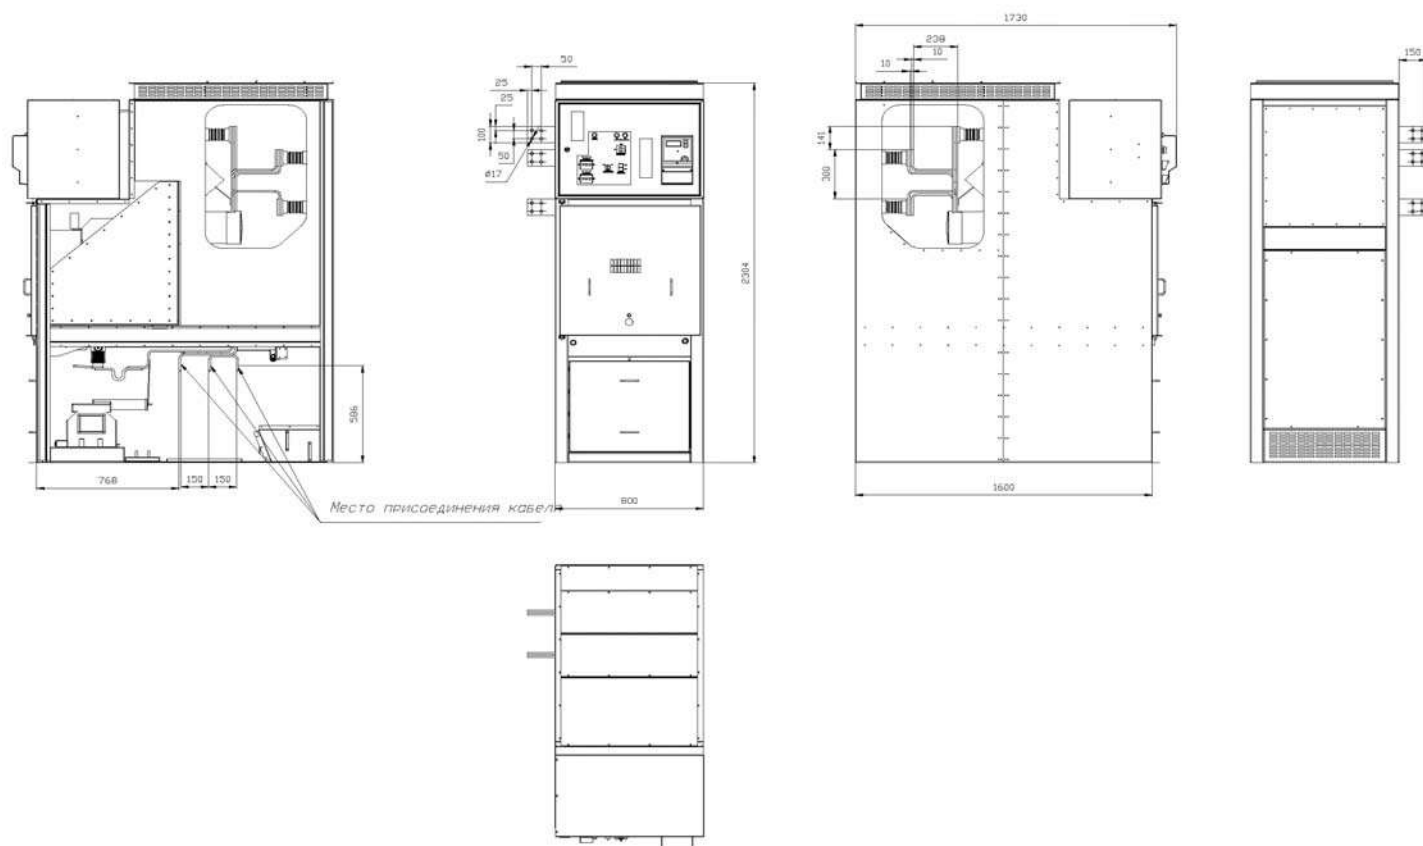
Общий вид и габаритные размеры КРУ2-СТ10
